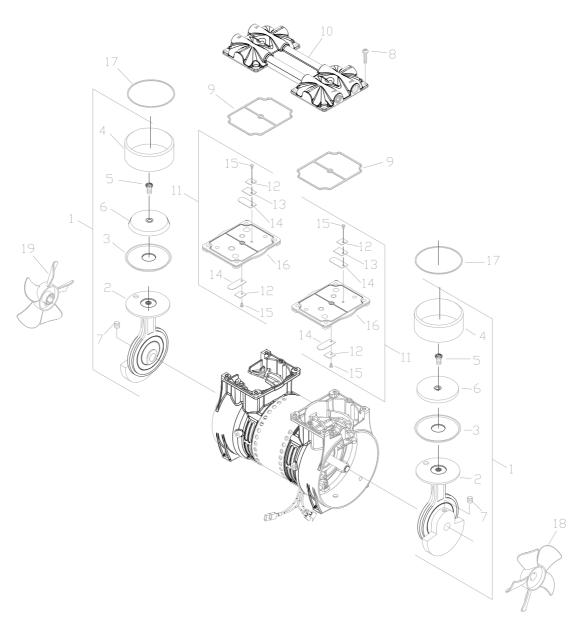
VUE ECLATEE COMPRESSEUR
